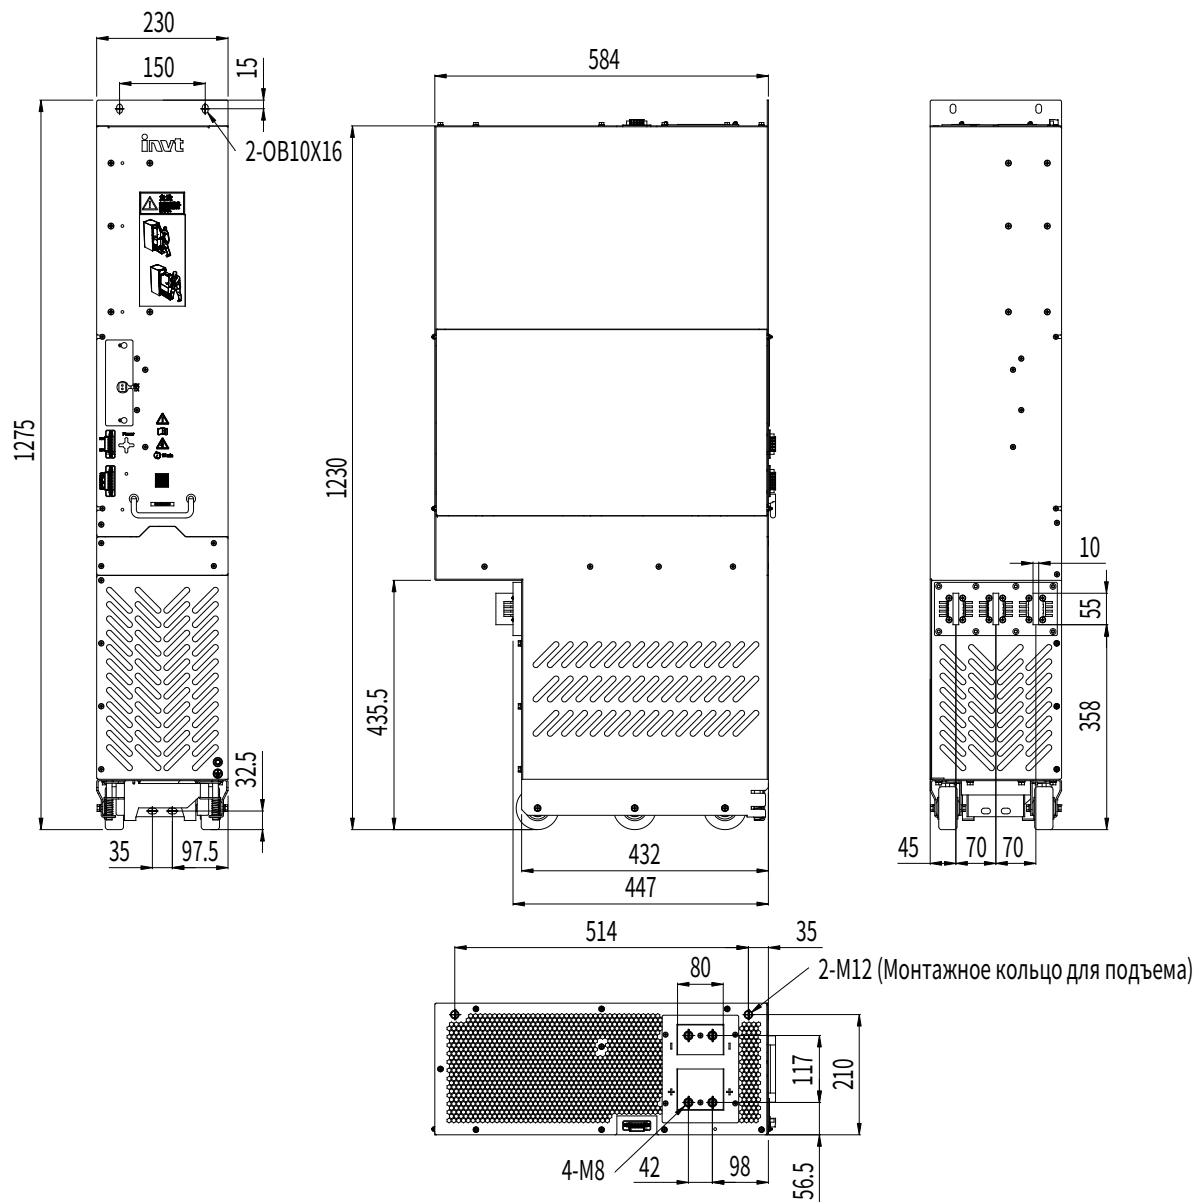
Установочные размеры быстродействующего разъема блока А8i (единица измерения: мм)
